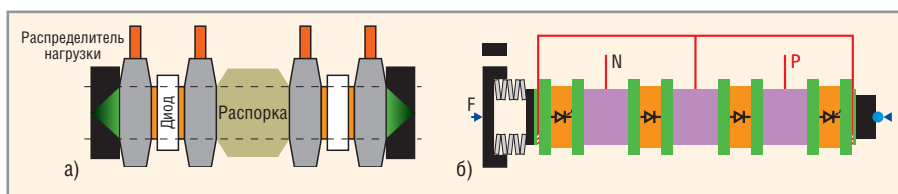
Удачно скомпонованная сборка с эффективными распределителями нагрузки и одинаковыми диаметрами приборов (а) и неудачная конструкция сборки с неэффективными распределителями нагрузки и различными диаметрами приборов (б)
